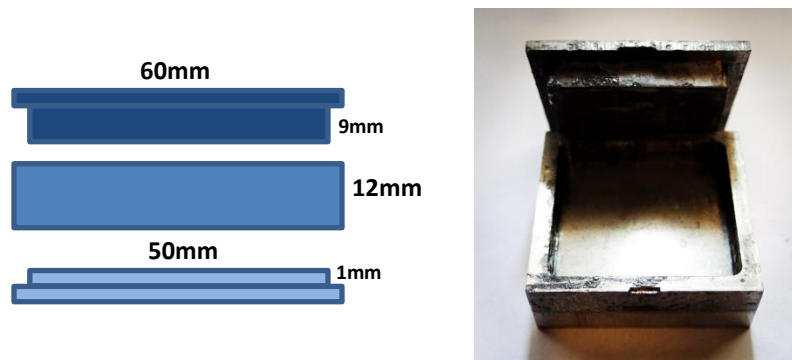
(izquierda) Dimensiones del molde y (derecha) fotografía del molde.
